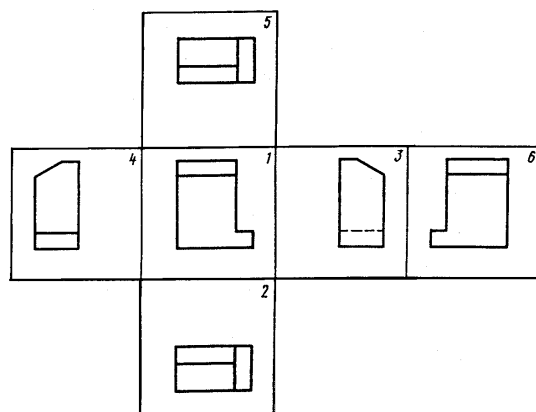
Основные виды: 1 – вид спереди (главный вид); 2 – вид сверху; 3 – вид слева; 4 – вид справа; 5 – вид снизу; 6 – вид сзади
